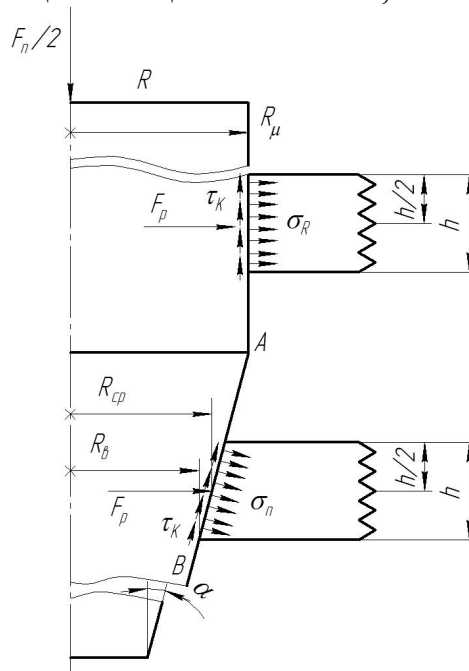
Розрахункова схема для циліндричної та конічної ділянок оправки.
